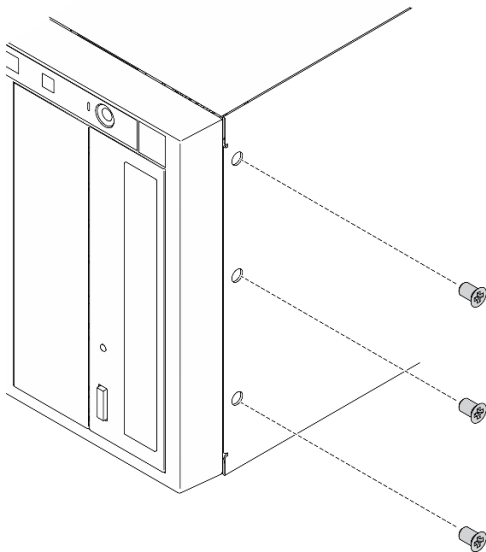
Entfernen der Schrauben an der Oberseite des Gehäuses
